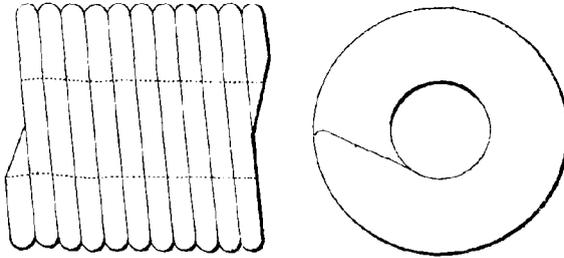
Enroulage pour la fabrication des bandages en fer.
